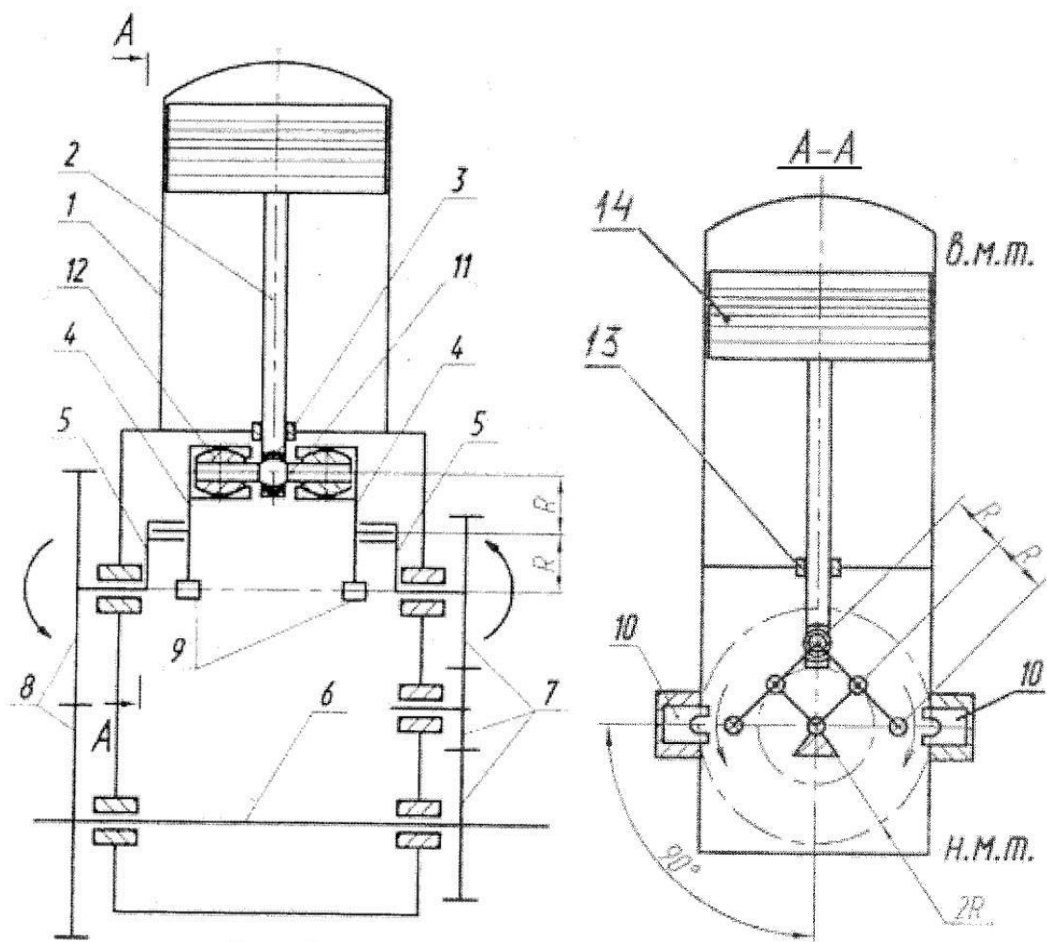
Схема ромбічного кривошипно-планетарного поршневого механізму:
